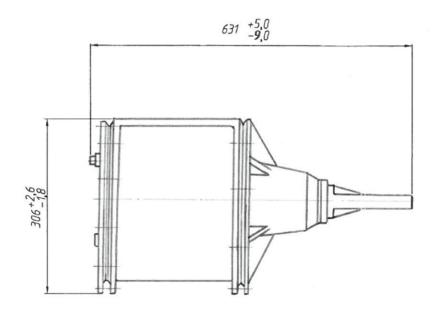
Общий вид тормозного цилиндра 710
